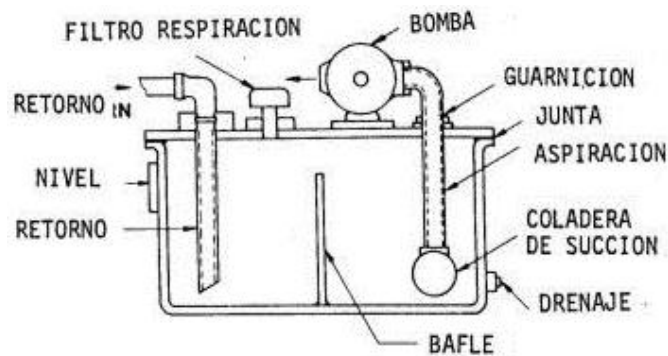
Vista frontal partes de un tanque hidráulico.
